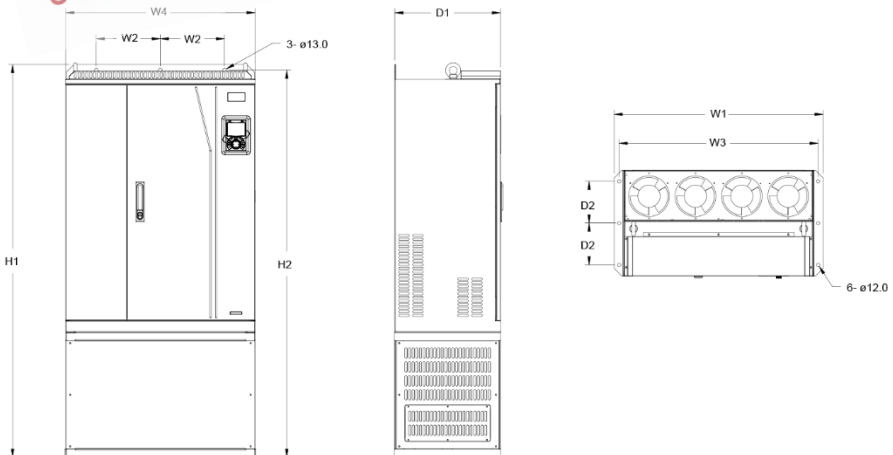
Схема для підлогового монтажу ПЧ напругою 380 В, потужністю від 220 до 315 кВт
